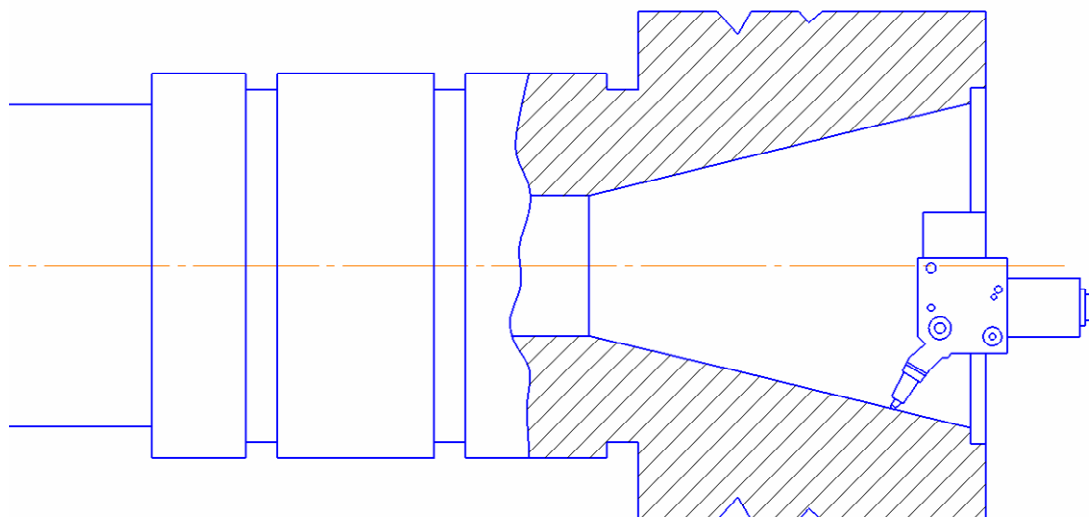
Пример раскатывания конической поверхности шпинделя фрезерного станка 6Р81
